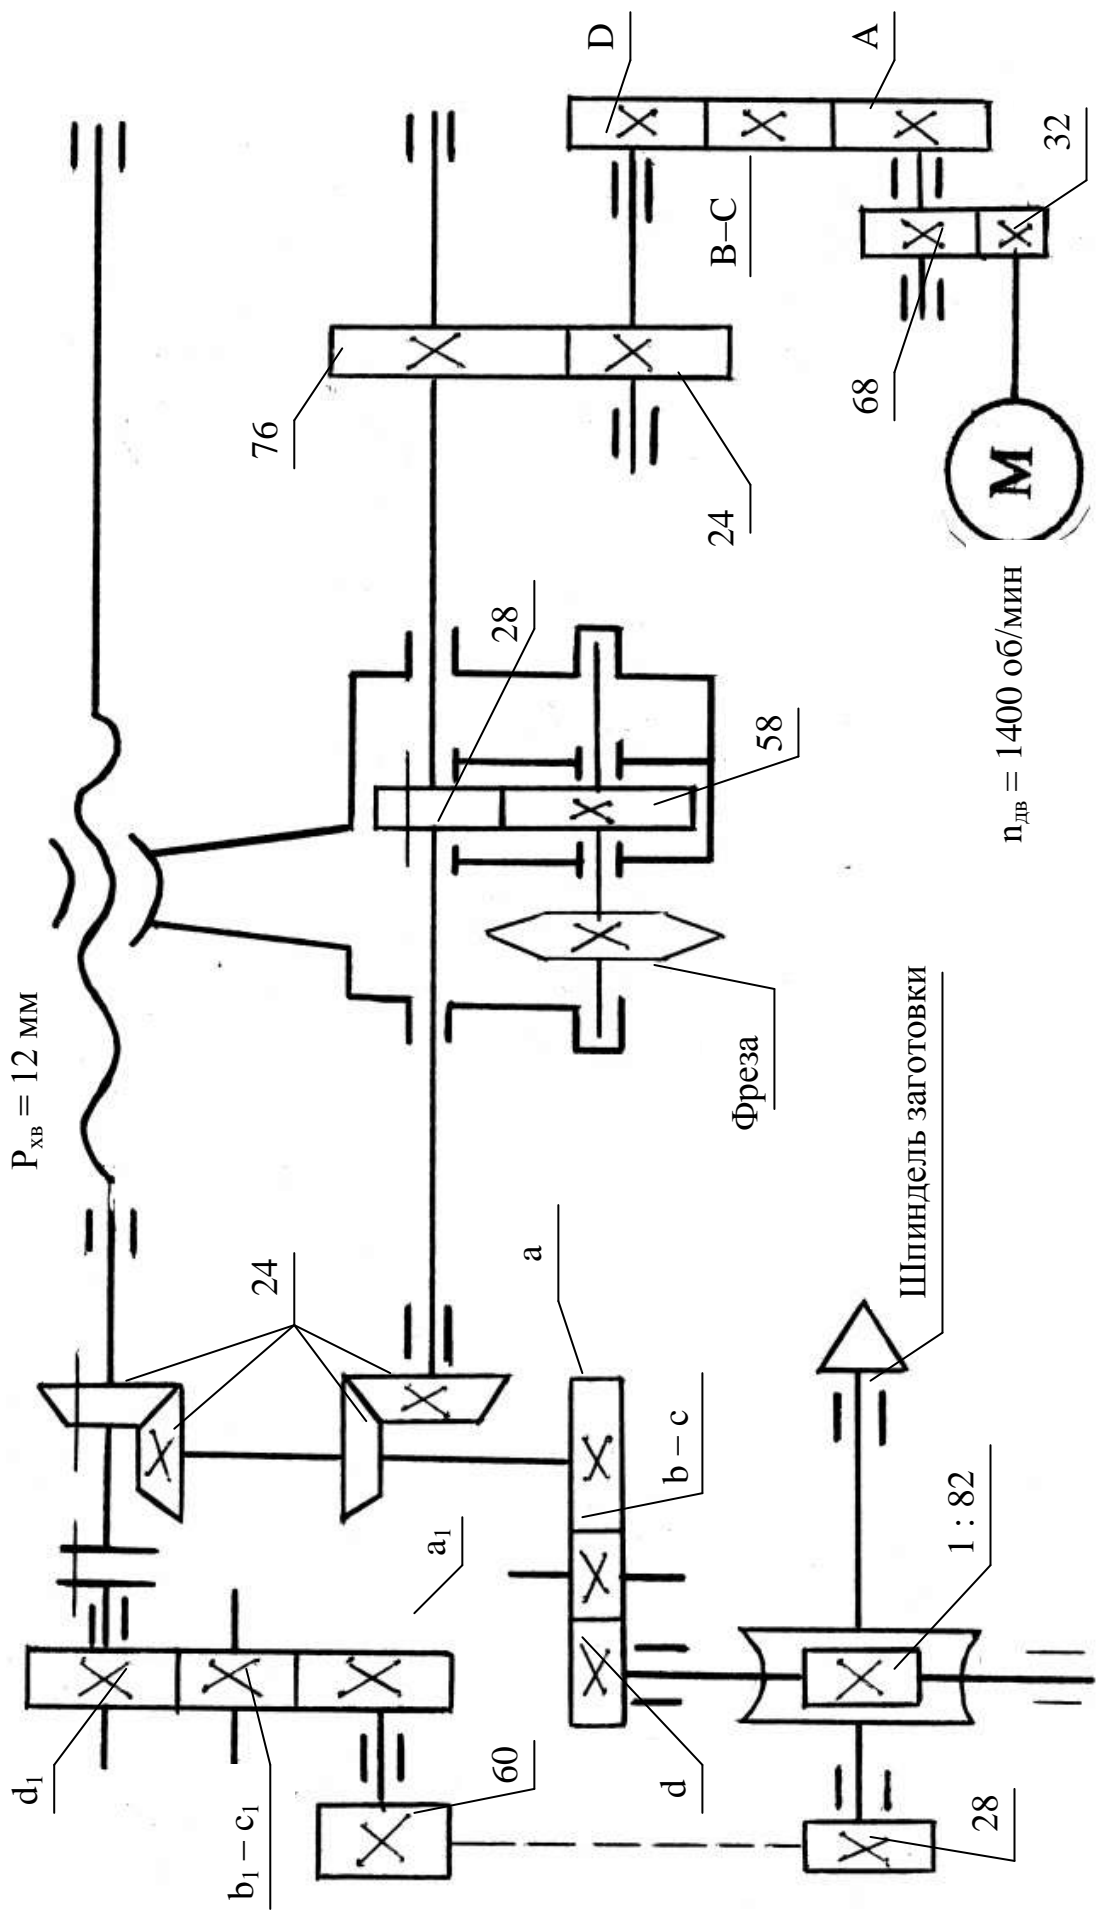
Кинематическая схема резьбофрезерного станка:
